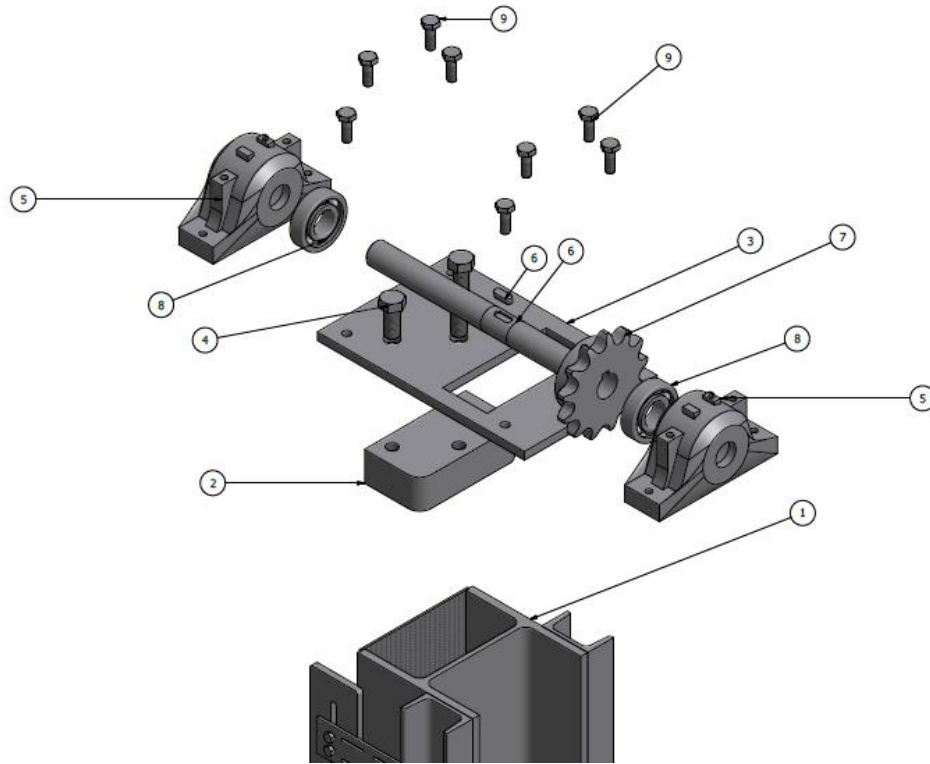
Despiece del Ensamblaje de la Plancha Superior y Componentes
